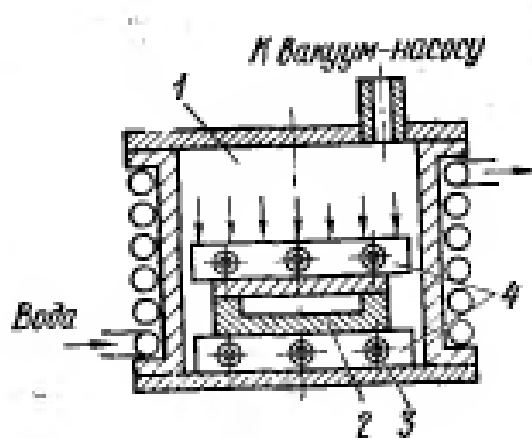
Схема установки для диффузионной сварки в вакууме:
